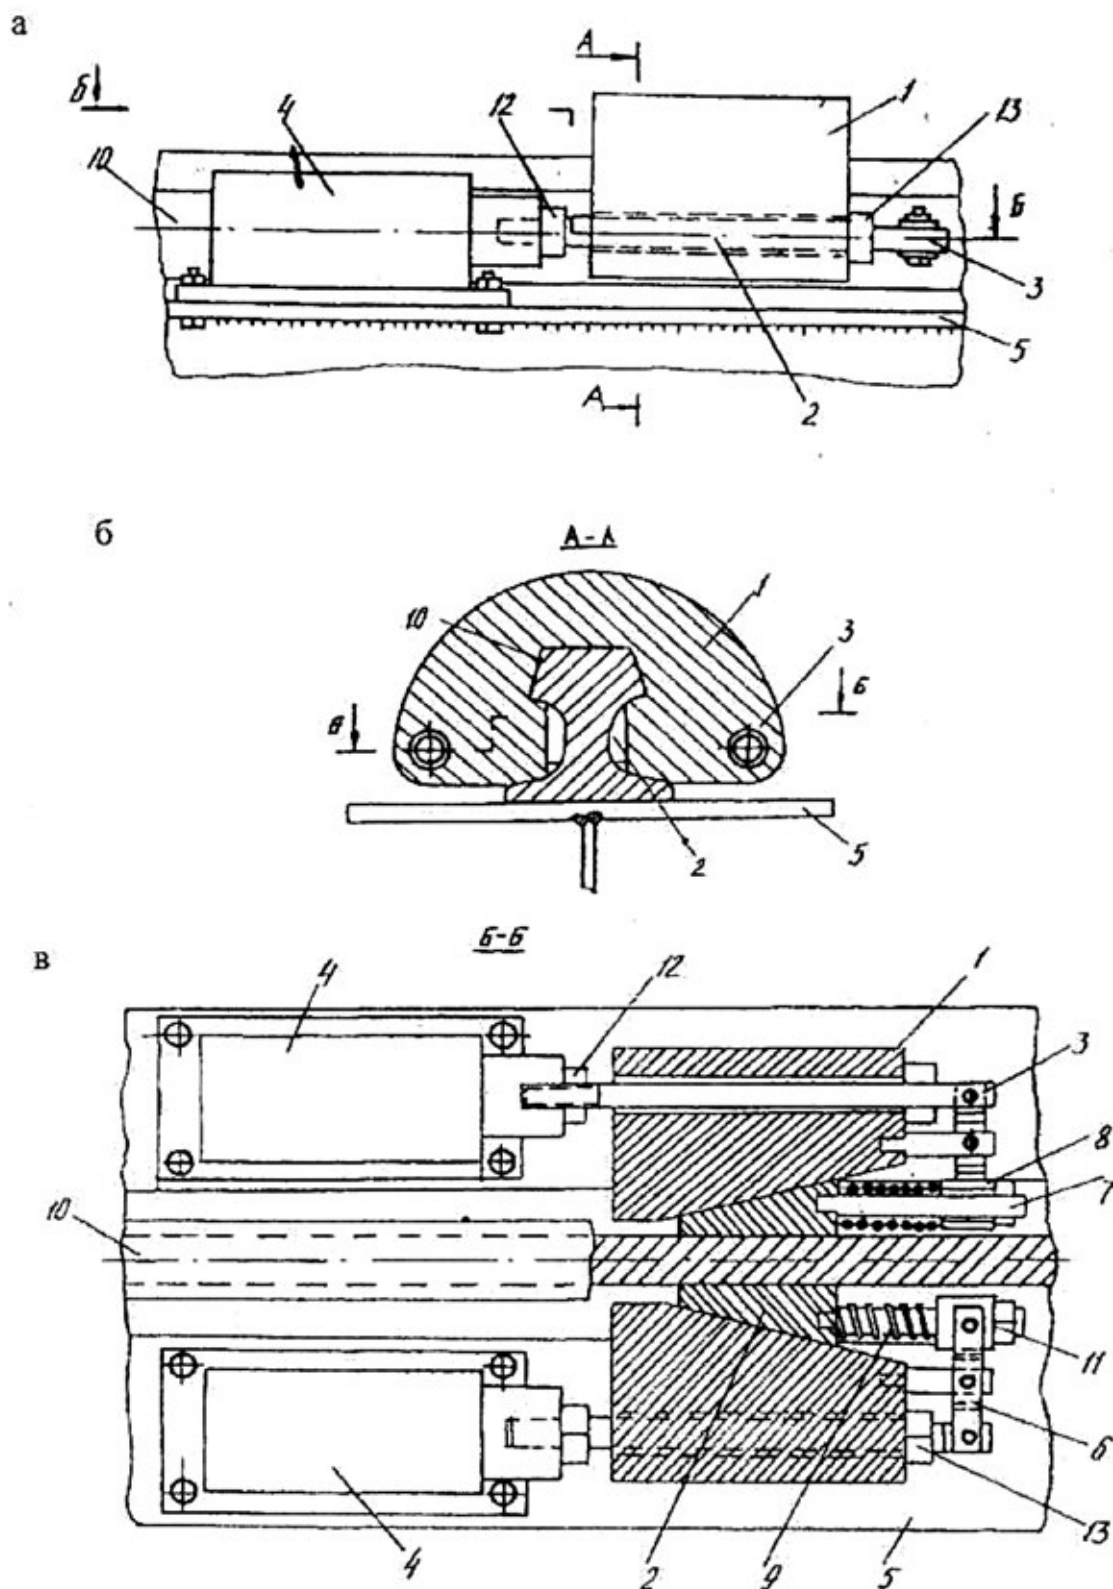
Автоматическое устройство для захвата и продольного перемещения плети рельсов:
